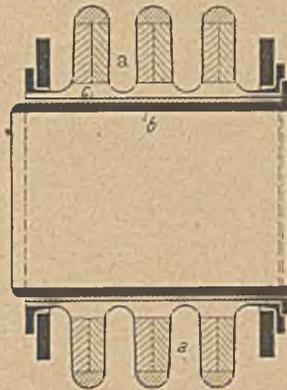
Ausgleichstück für die Auspuffleitung einer Gasmaschine.
